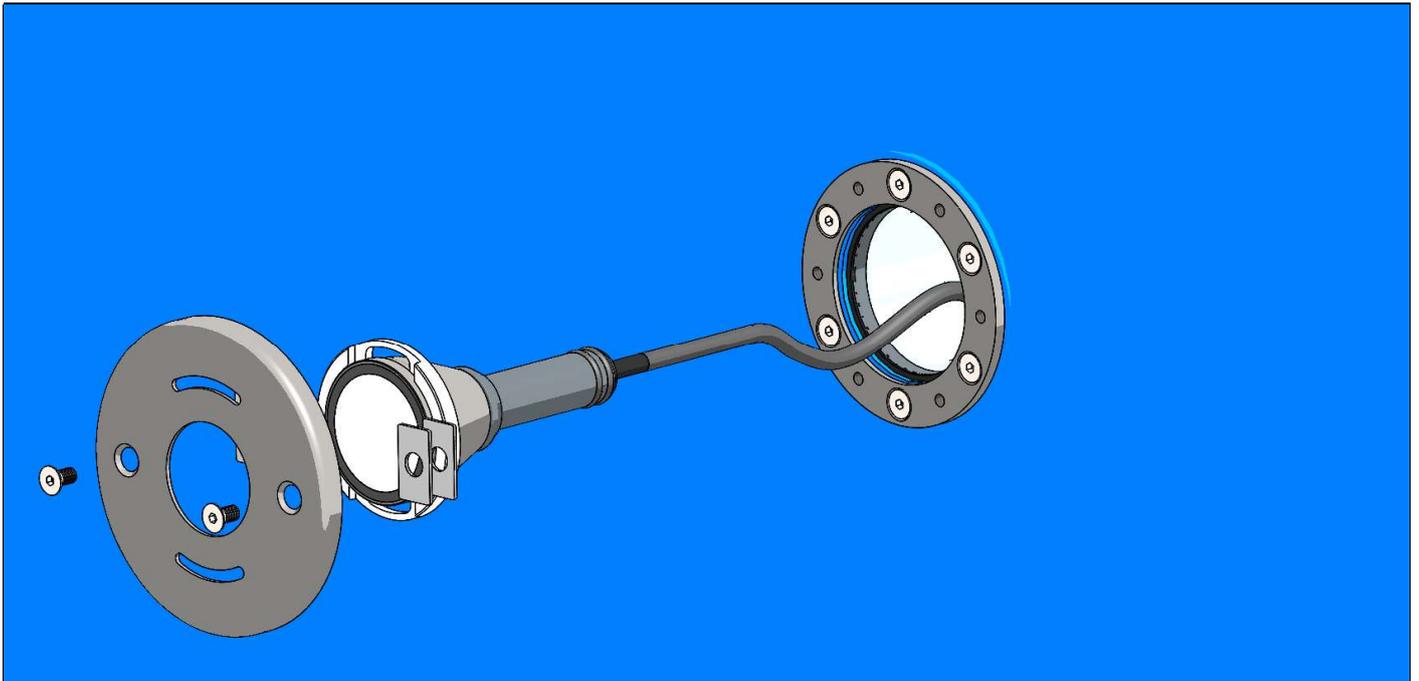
Fertigmontage Betonbecken mit Folienabdichtung
